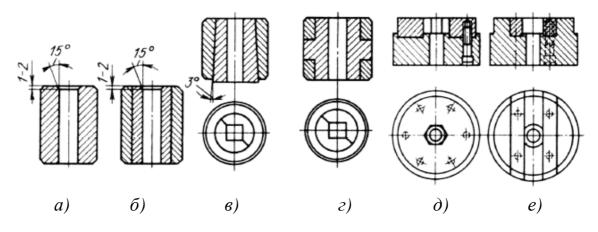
Виды матриц для холодного прессования порошков
